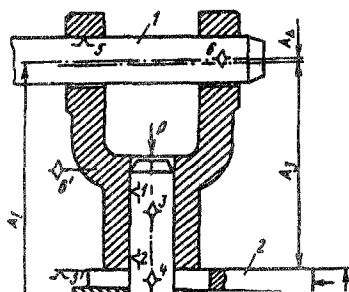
Варианты схем базирования в приспособлениях для сборки втулки с корпусом при необходимости выдерживания размера A
